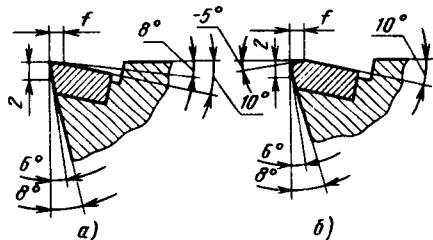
Конструктивное оформление передней поверхности твердосплавных резцов
